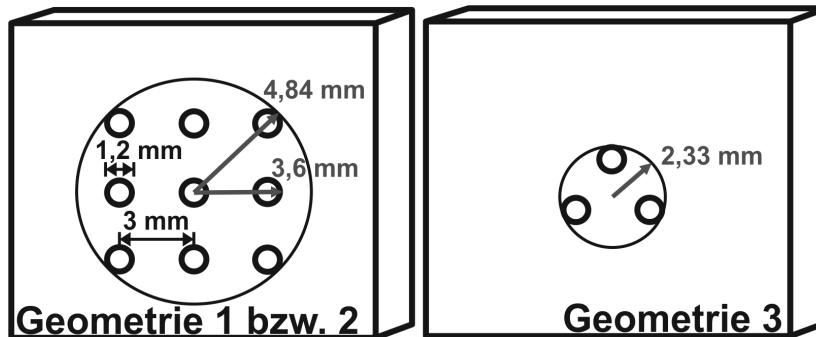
Mindestabmessungen für die Wahl der Einhüllenden für die jeweilige Bohrgeometrie mit Einzelfehlerdurchmesser 1,2 mm.
